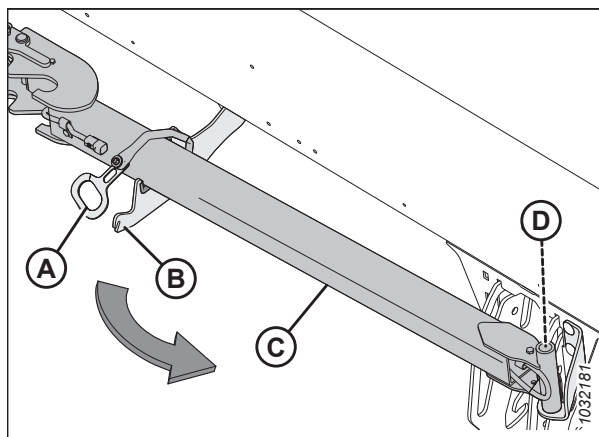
Extensión de la barra de remolque en almacenamiento
